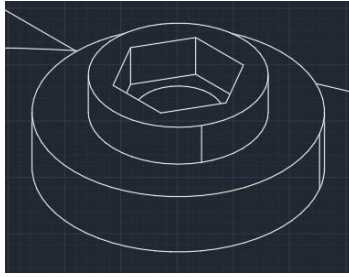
Vista en 3 dimensiones del dado para válvulas de gas.
